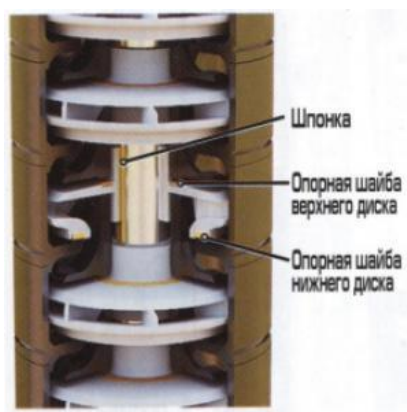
Насос с «плавающим типом» рабочих колес в разрезе
